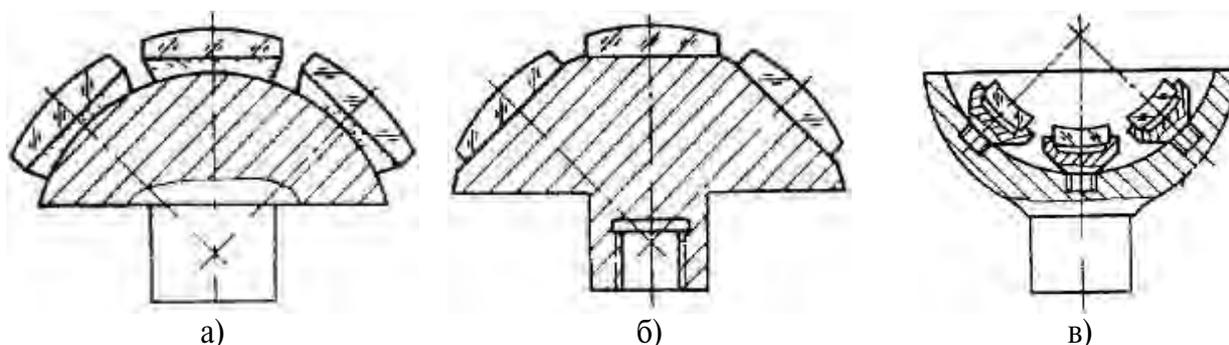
Наклеечные приспособления для крепления линз:
